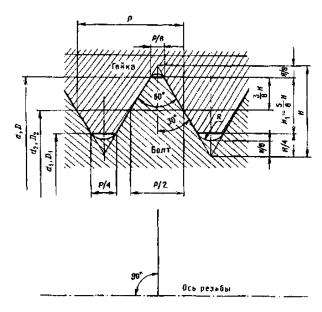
Профиль метрической резьбы и ее основные параметры
